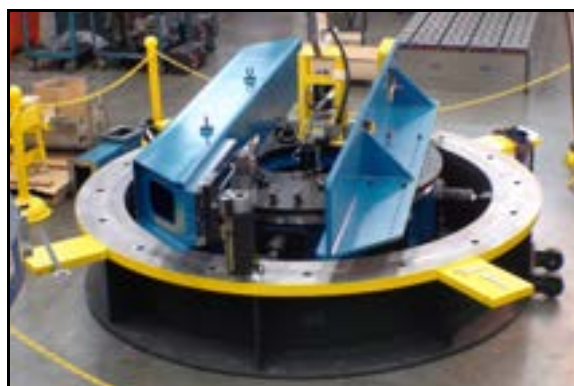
MONTAGE HORIZONTAL DE LA MACHINE
